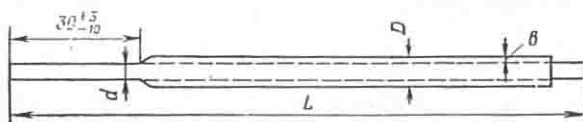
Сварочный электрод для дуговой сварки (ГОСТ 2523—51)
